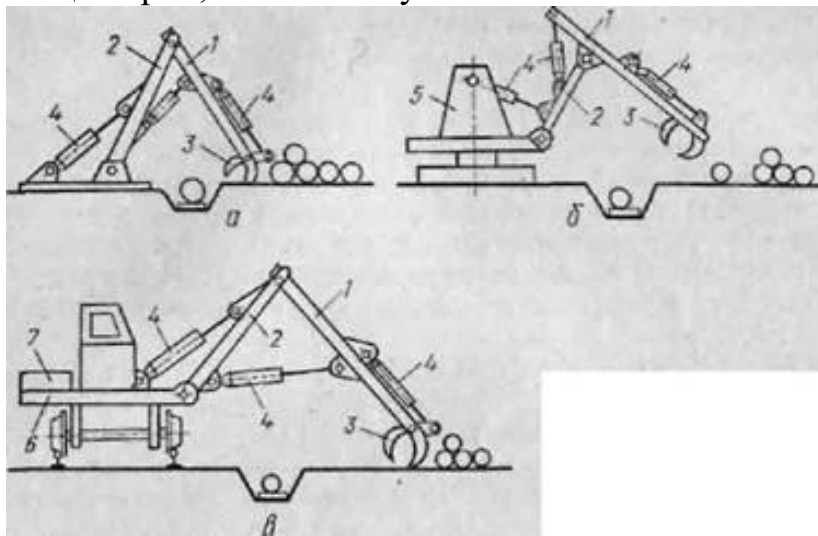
Типи маніпуляторів: 1 - рукоять стріли; 2 - стріла; 3 - кліщовий захват; 4 - гідроциліндр; 5 - поворотна колона; 6 ходовий візок; 7 - противагу
